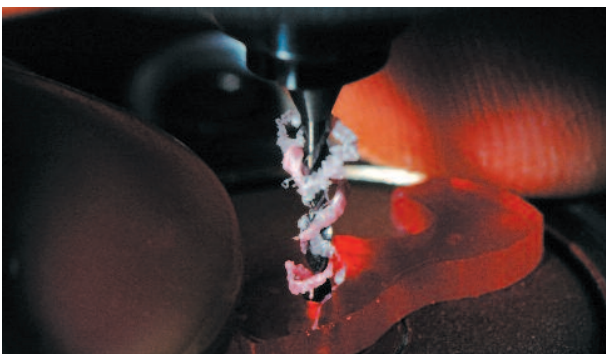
Das Bohren für die Achse (Durchmesser 1,5mm).
